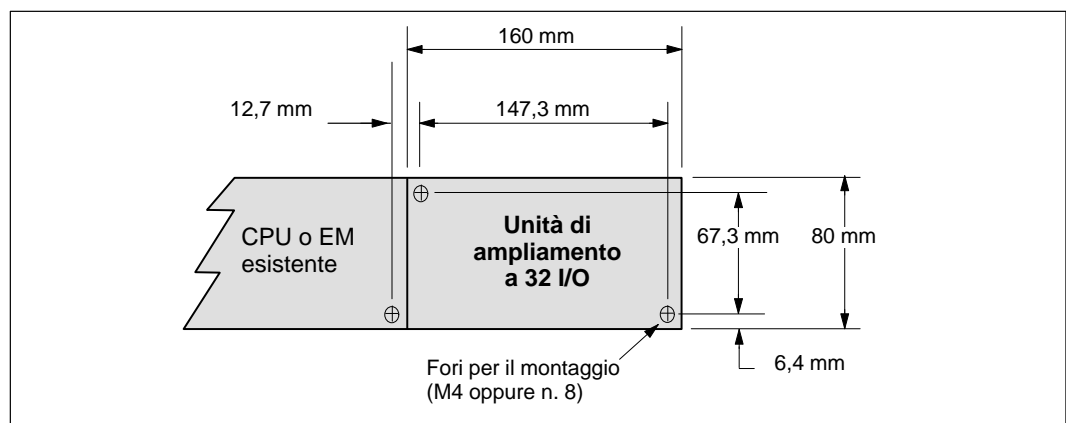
Dimensioni per il montaggio di una unità di ampliamento a 32 I/O
